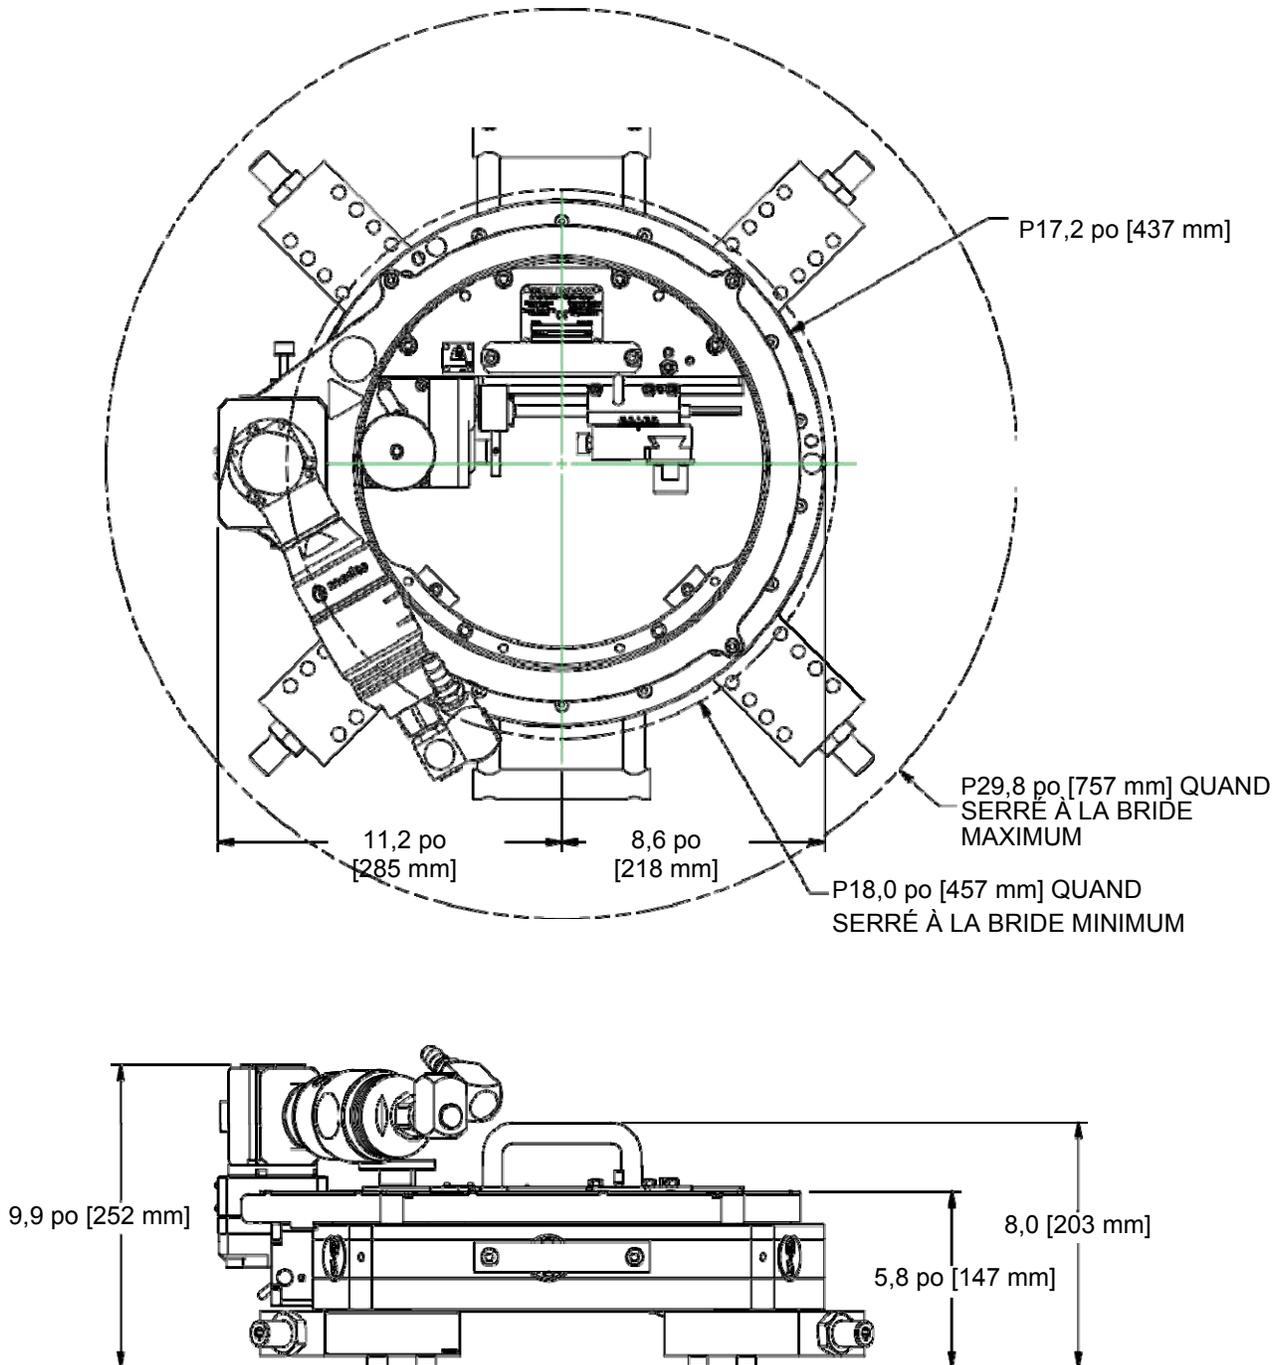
DIMENSIONS DE LA MACHINE FF1200
